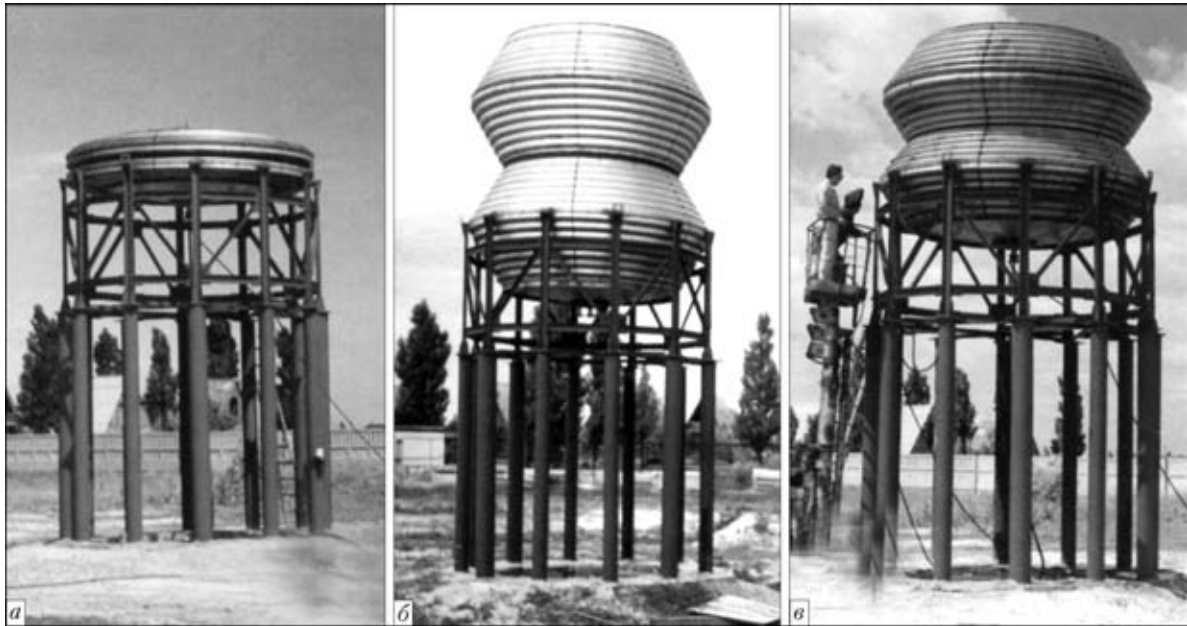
Вид крупногабаритной сварной конструкции преобразуемого объема перед (а), в процессе разворачивания (б) и полностью развернутой (в)
